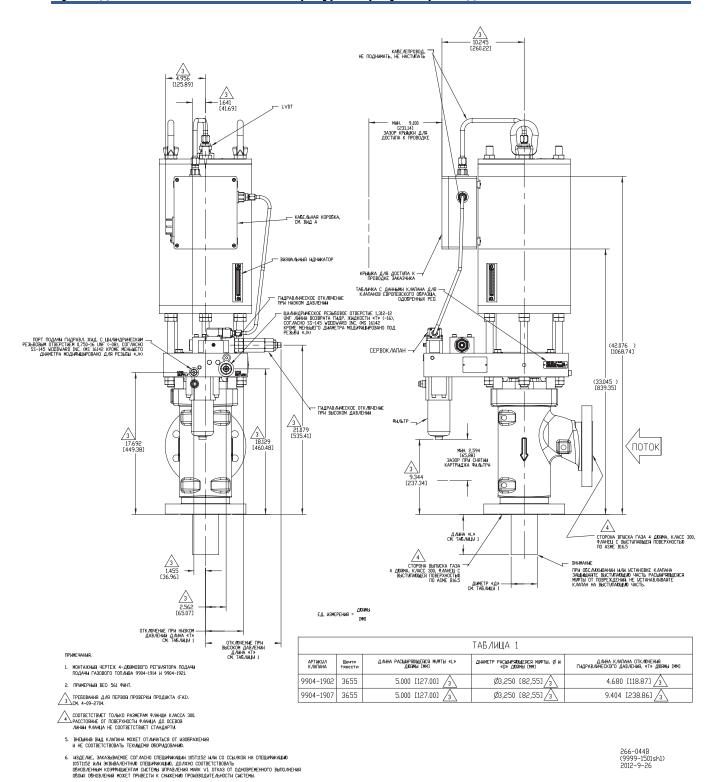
Габаритный чертеж регулятора SonicFlo (4 дюйма, класс 300)
